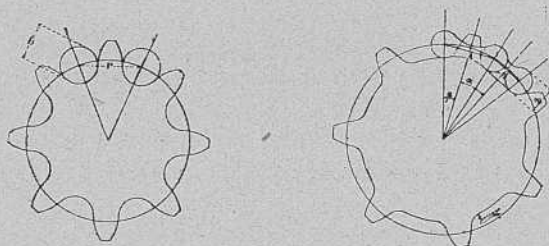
y 630.—Ruedas para cadenas de rodillos equidistantes y rodillos gemelos.
